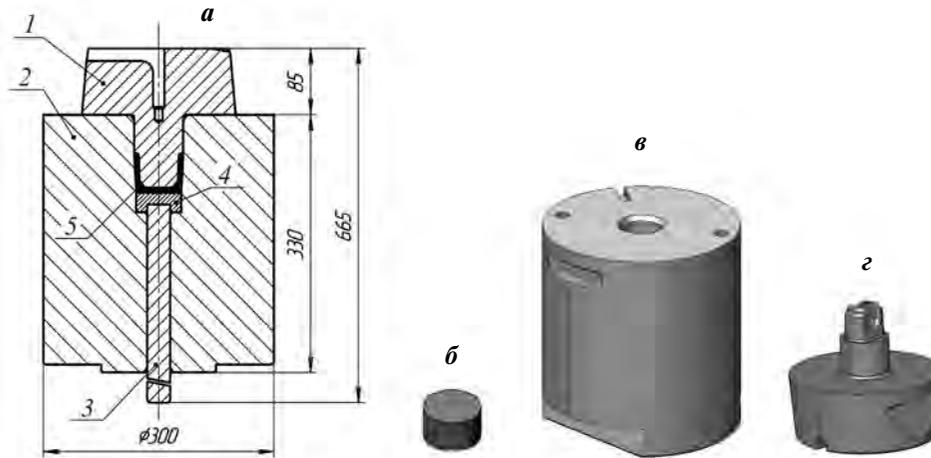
Сборочный чертеж штампа (а) и модели заготовки (б), матрицы (в) и пуансона (z)
